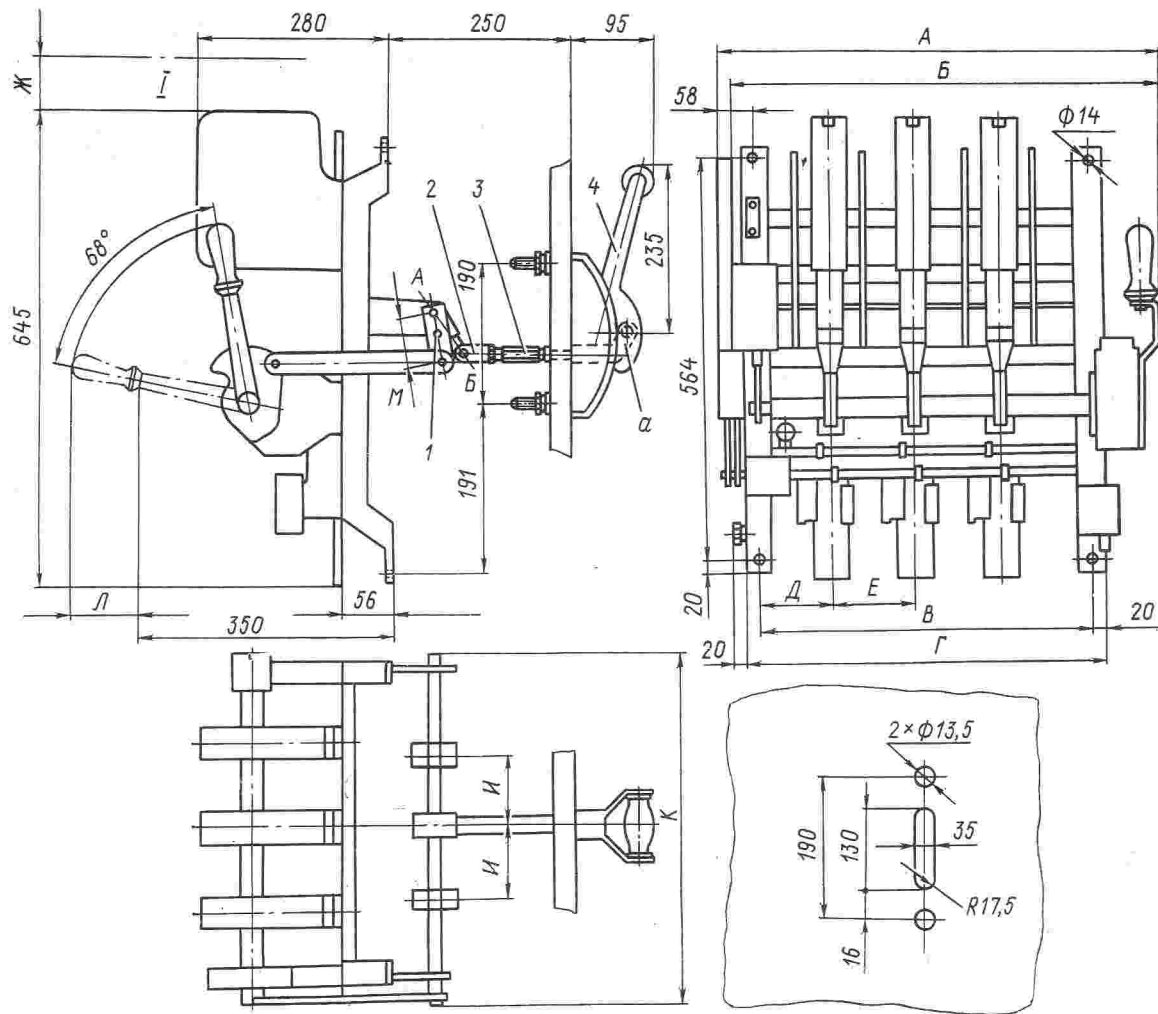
Габаритно-установочные размеры стационарных выключателей с рукояткой и рычажным приводом:
